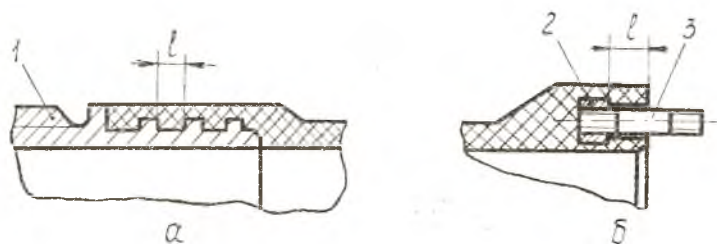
Конструкция закладных элементов: *a* — для резьбового соединения; *б* — для фланцевого соединения: 1 — элемент с резьбой; 2 — закладное кольцо; 3 — шпилька
